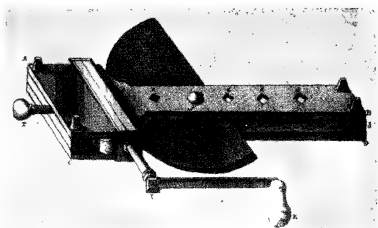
Инструмент для накатки зубьев на секторах мелких червячных зубчатых колес. 1760 г. По Цейгеру.
